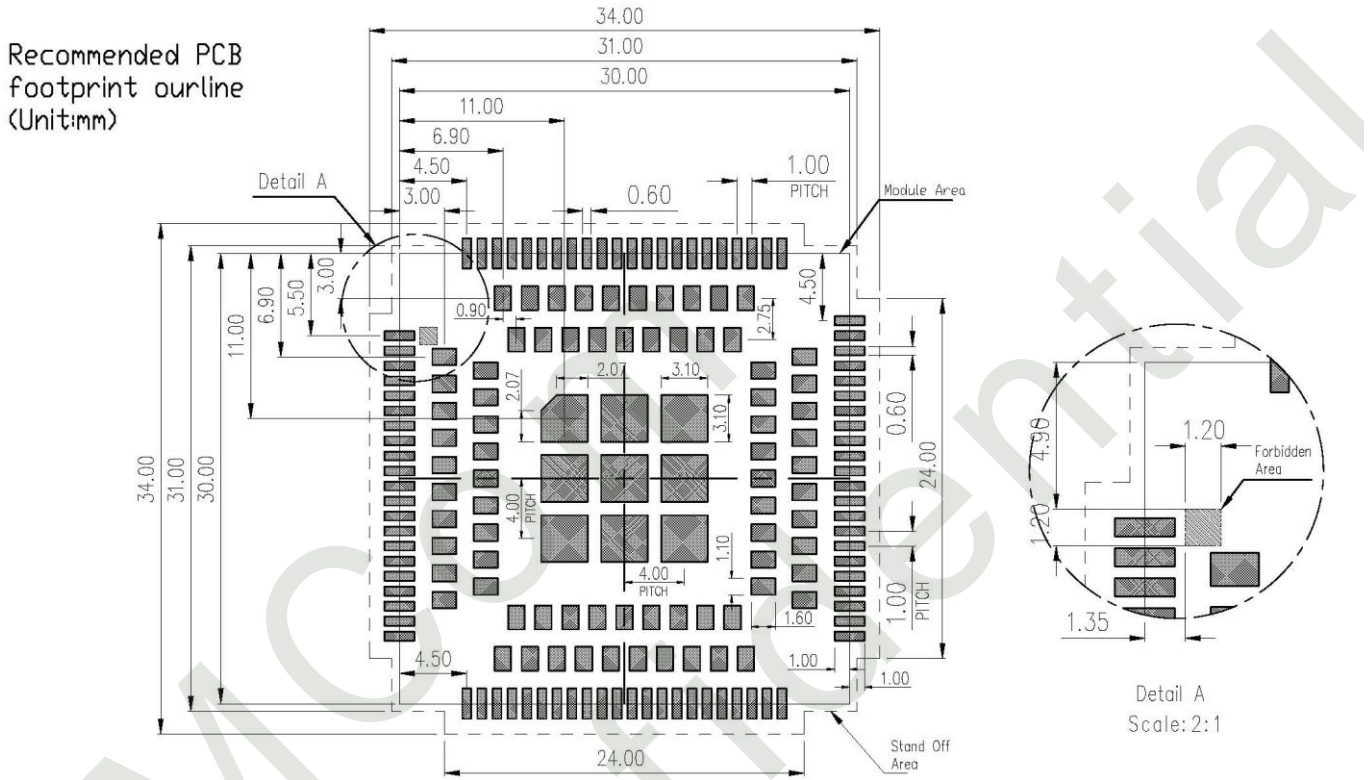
推荐 PCB 封装尺寸(单位: 毫米)
